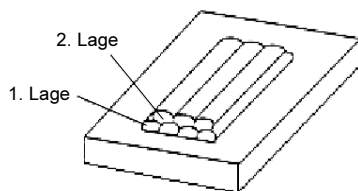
Prüfstück Form 1; 2-lagige-Auftragschweißung.
